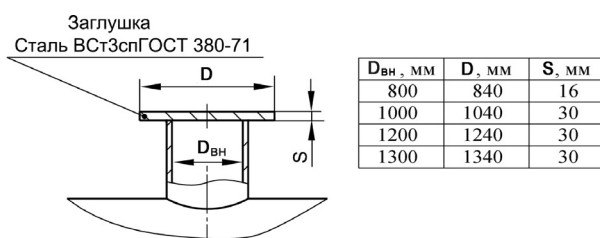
Вид и основные размеры заглушки для отключения отверстий, штуцеров, вентилей и патрубков
